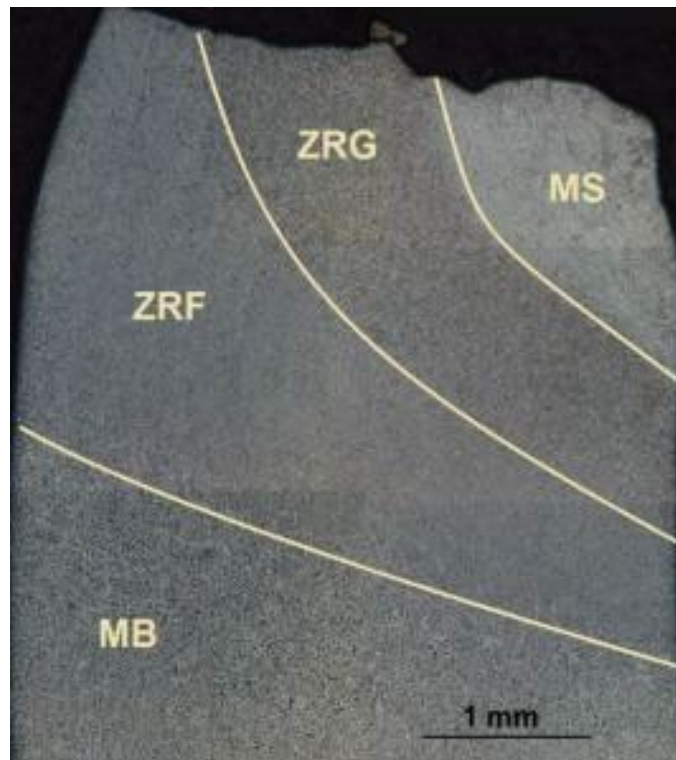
Macrografía de corte transversal de sección de soldadura analizada. Fuente: investigación JST
